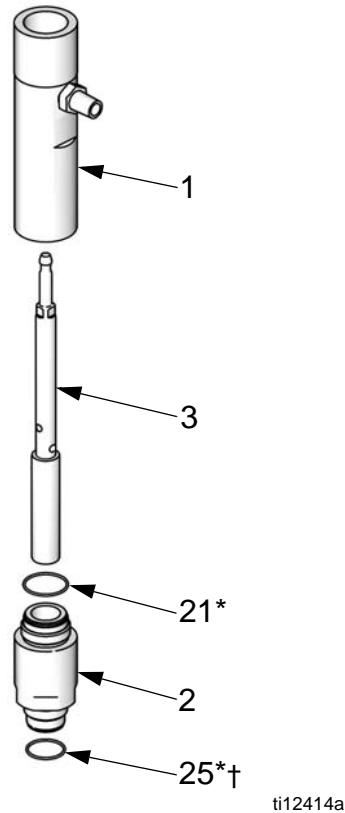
Assemblare il gruppo pistone/biella e i cilindri.
